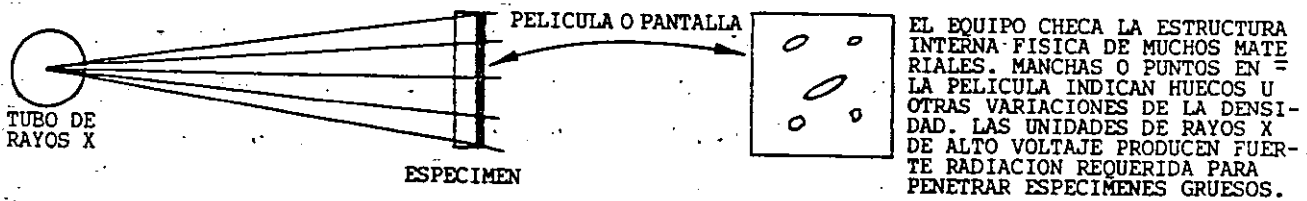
FIG. ESQUEMA DE UNA FOTOGRAFIA DE RAYOS X A UNA SOLDADURA.
